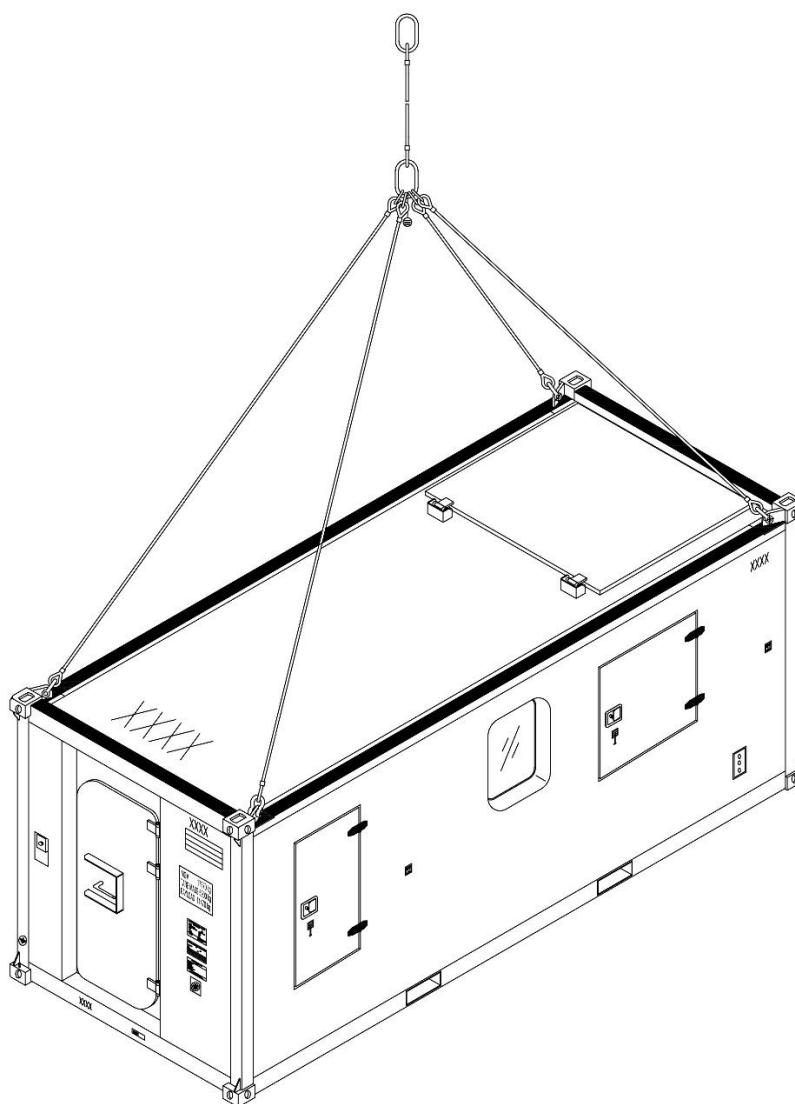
Офшорный сервисный модуль с подъемным приспособлением
